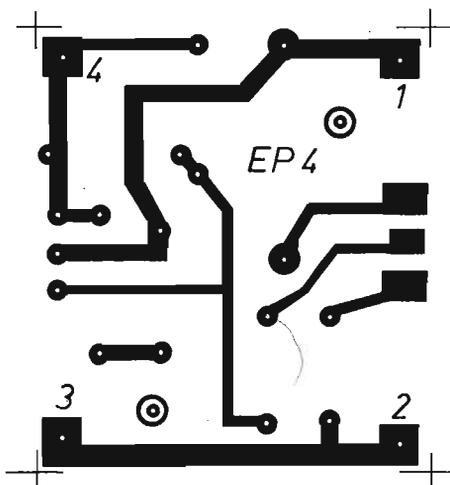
Disegno in grandezza reale del circuito stampato da riportare su una delle due facce di una basetta supporto rettangolare delle dimensioni di 6 cm x 5,3 cm.
